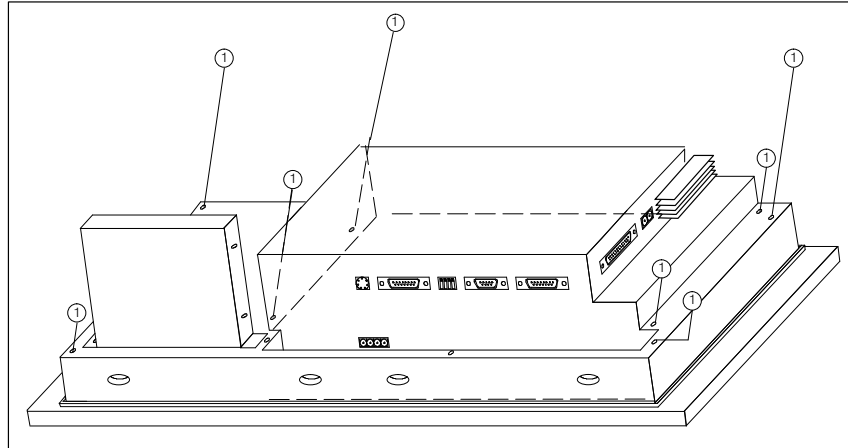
Schrauben der äußeren Gehäuserückwand lösen
